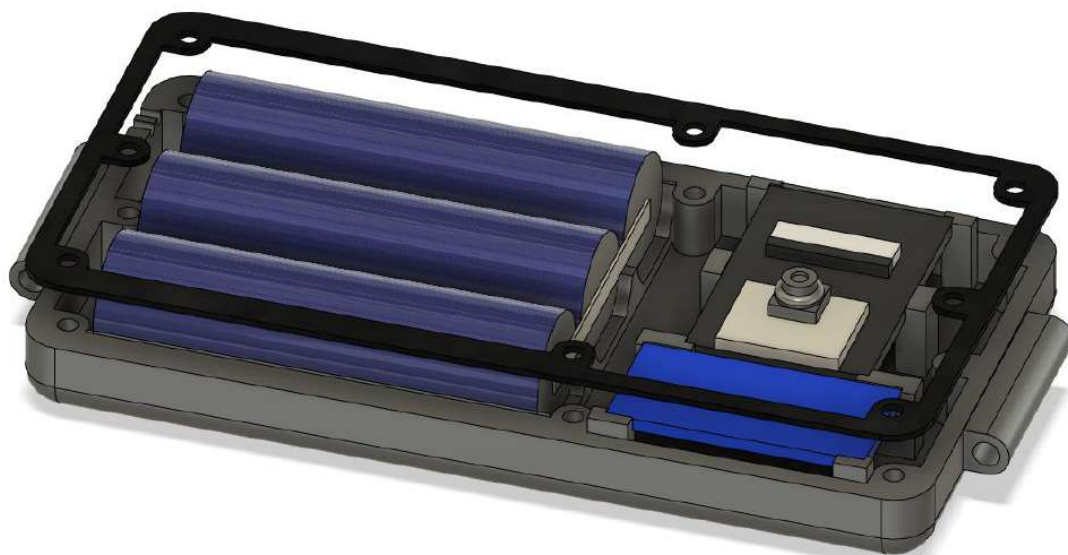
Резинова прокладка між частинами корпусу
